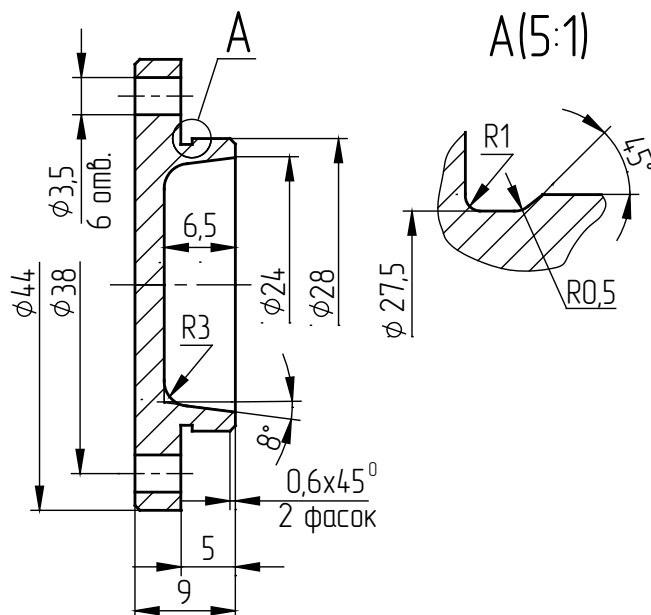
Учебный рабочий чертеж крышки, учитывающий все особенности ее конструкции (без упрощений)
